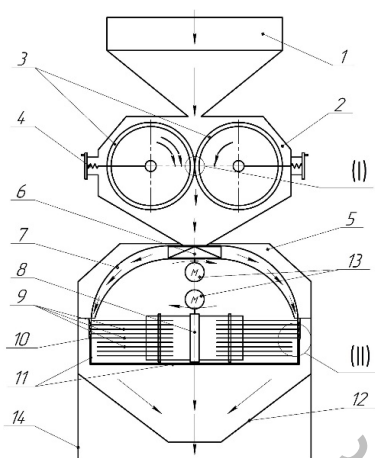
Общий вид устройства для двухстадийного измельчения зерна
